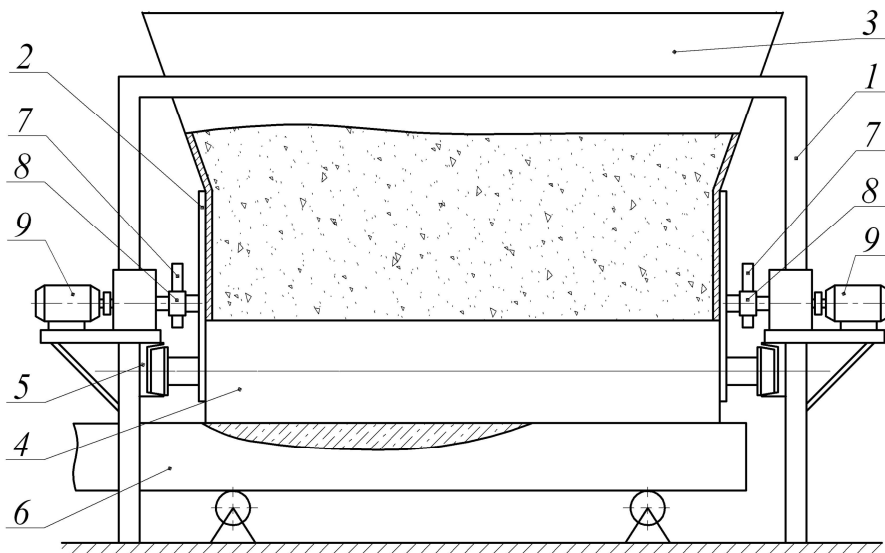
Роликова формувальна установка з двома кулачковими приводними механізмами
